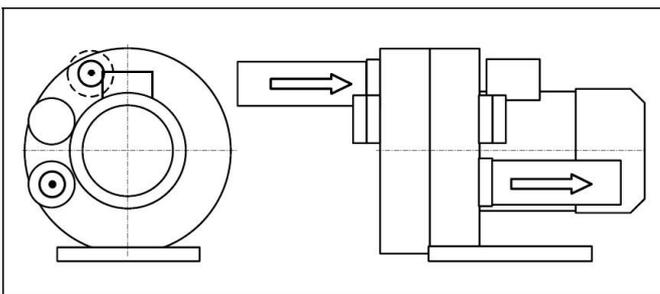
Двухступенчатые вакуумные насосы/компрессоры с двумя рабочими колесами
